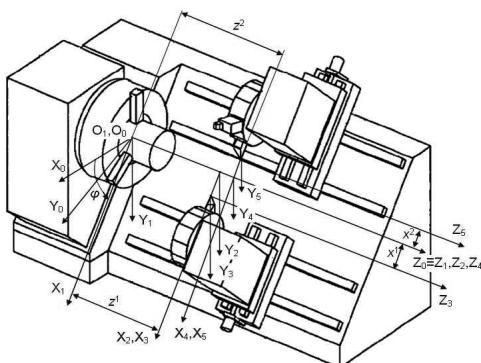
Формоутворююча система одношпиндельного двосупортного токарного верстата з ЧПК
